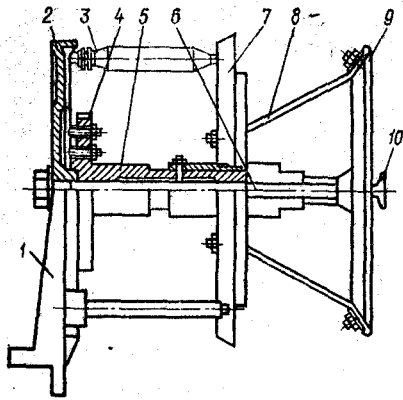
Схема барабанного магазина станка АТ-100-5М
